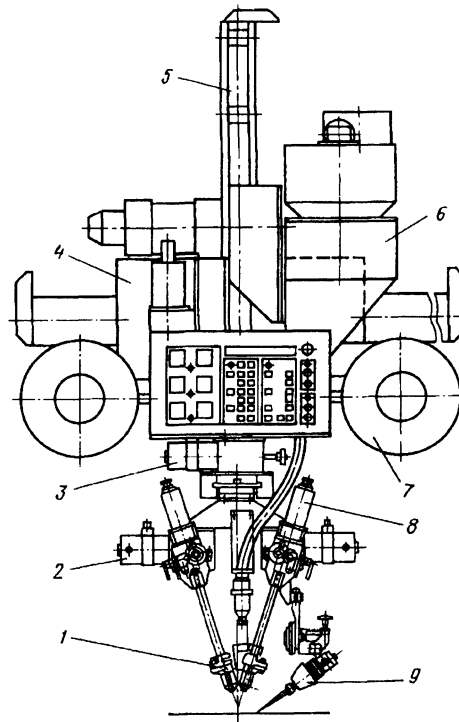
Автомат АД380.05.00.000 для сварки трехфазной дугой
